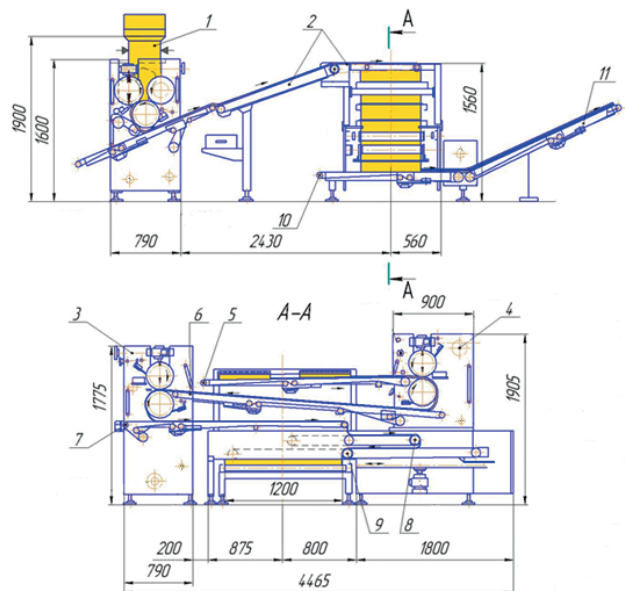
Схема установки УШП-ЛС600 для отримання багатшарового пласту із зтяженого тіста: 1 — тривалкова машина; 2 — розвальний пристрій; 3, 4 — відповідно правий і лівий двовалкові ламінатори; 5 — горизонтальний транспортер; 6 — похилий транспортер; 7 — нижній транспортер; 8, 9 — відповідно верхній і нижній транспортери каретки укладача листів; 10 — транспортер для розкладених листів; 11 — підйомний транспортер.
